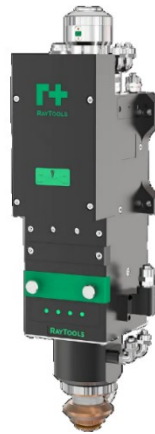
Загальний вигляд лазерної головки з автофокусом RayTools BS12K
